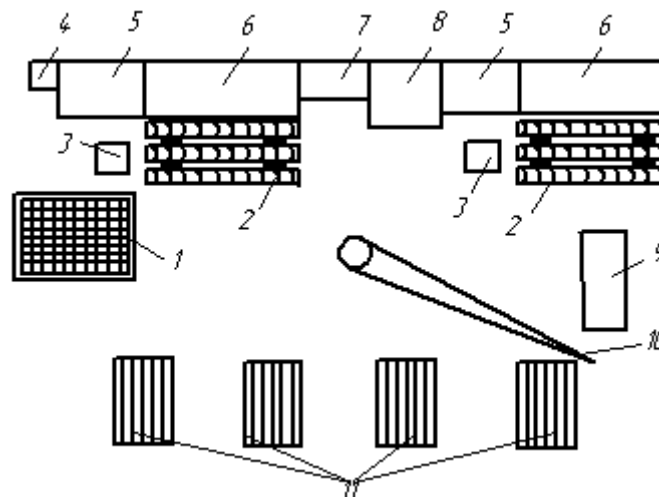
Типовая планировка рабочего места бригады слесарей-сборщиков: 1 – подставка для деталей; 2 – решетки под ноги; 3 – подъемно-поворотные стулья; 4 – урна; 5, 11 – столы; 6 – слесарные двухтумбовые верстаки; 7 – двухсекционный шкаф; 8 – стол для технической документации; 9 – стеллаж; 10- консольно-поворотный кран.
